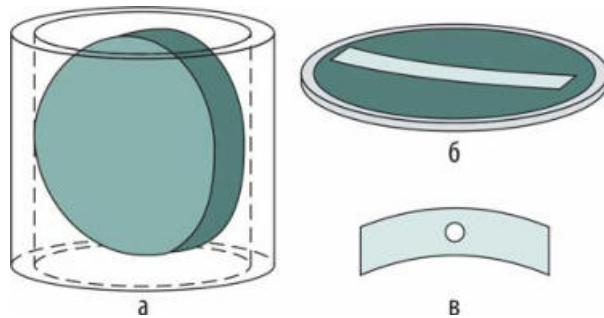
Общий вид заготовки в обойме перед заливкой эпоксидной смолы (а) и после шлифовки (б) и готового образца с полученным отверстием (вид сверху (в))
